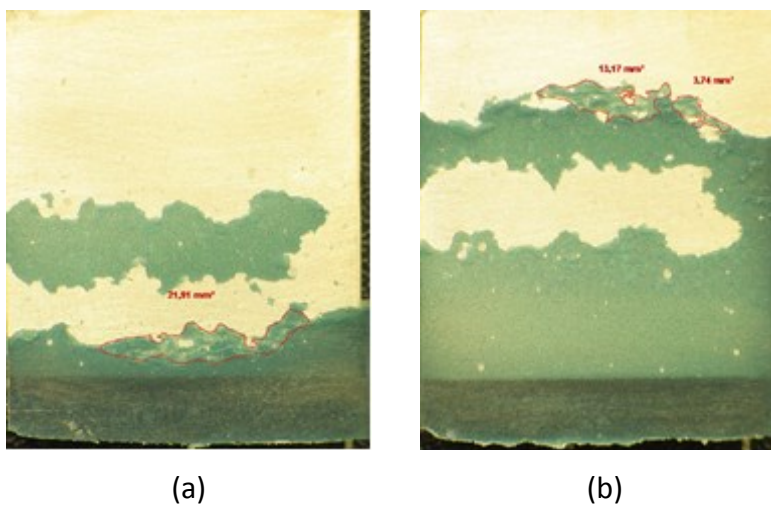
Provete 1 com "taper" em adesivo 45°. Superfície 1(a), Superfície 2 (b).
